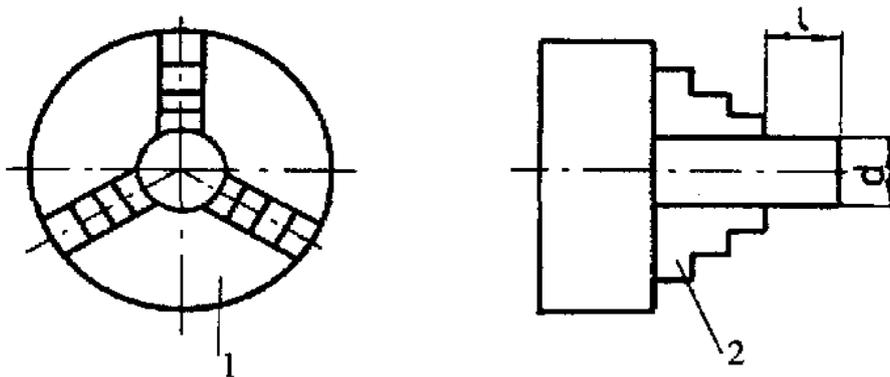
Схема установки заготовки в трёхкулачковом патроне
